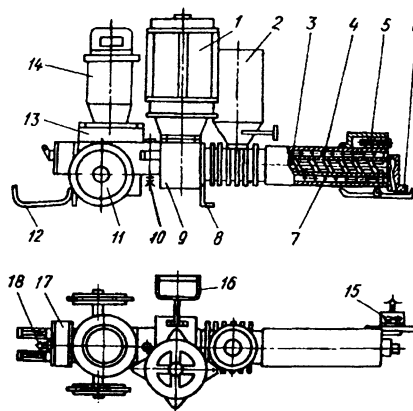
Сварочный аппарат установки ПЭСУ-2000:
